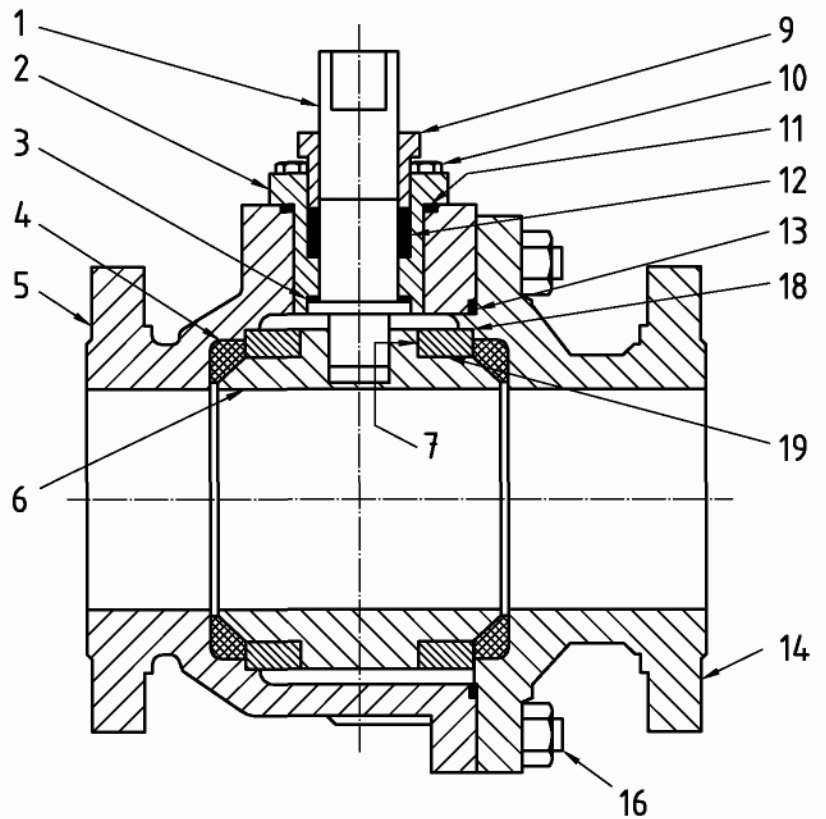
Типовые компоненты цапфового шарового крана (показан разъемный корпус) — Номенклатура
